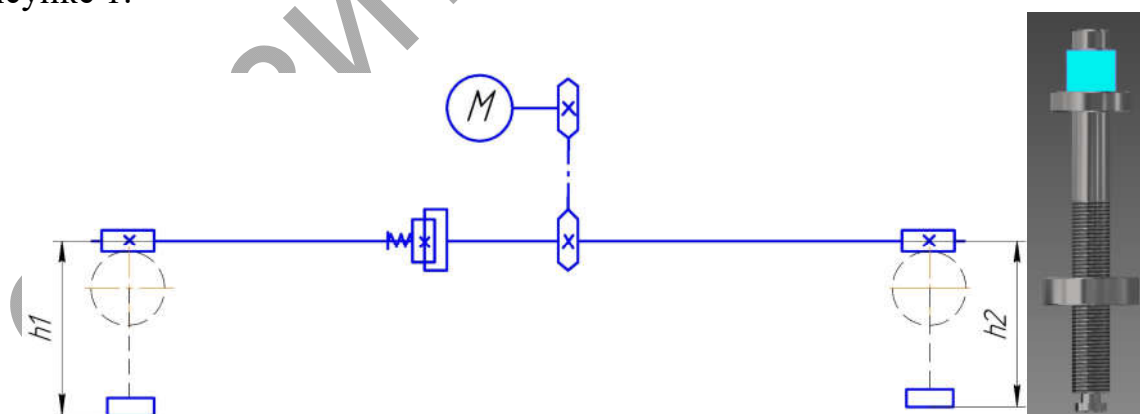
Упрощенная кинематическая схема настройки и поверхность закрепления вала
